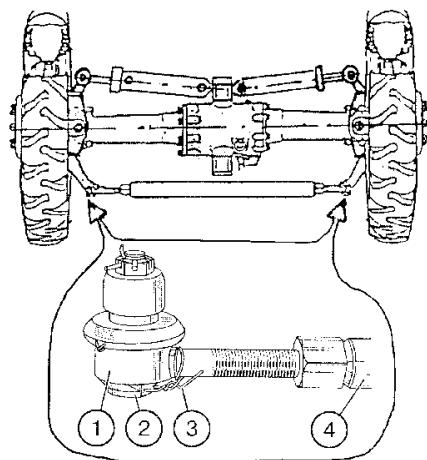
Проверка люфта в шарнирах рулевой тяги: 1 – шарнир; 2 – резьбовая пробка; 3 – контрольная проволока; 4 – рулевая тяга
